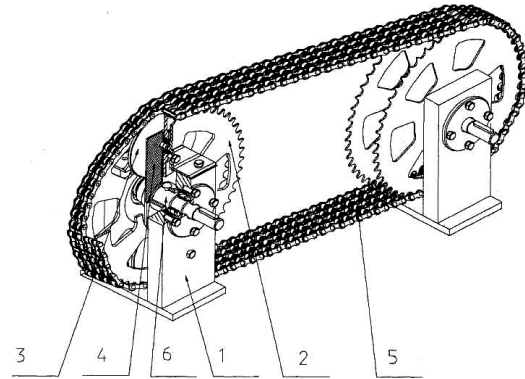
Хвильова ланцюгова передача: 1 – корпус; 2 – нерухома зірочка; 3 – катки; 4 – водило; 5 – ланцюг; 6 – приводний вал
